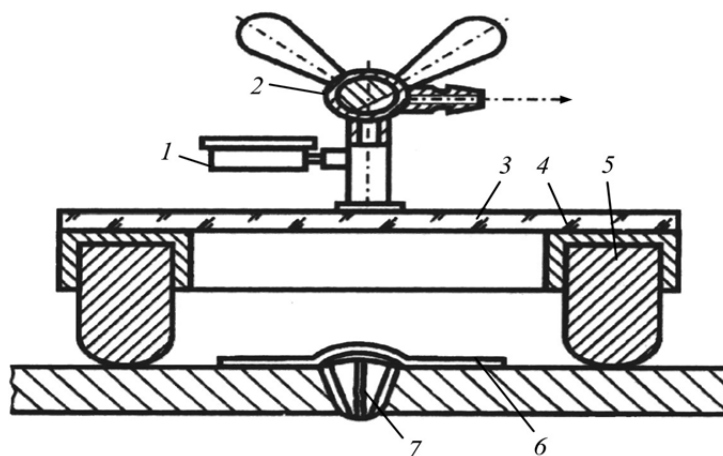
Прямокутна вакуум-камера: 1 — вакуумметр; 2 — триходовий кран; 3 — оргскло; 4 — металева рамка; 5 — гума; 6 — плівка піноутворюючої речовини; 7 — дефект
